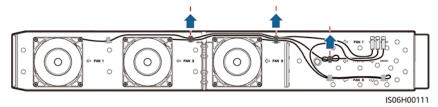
Desmontaje de las abrazaderas para cables del ventilador 1
